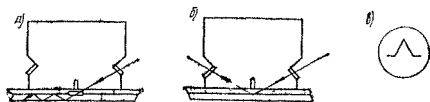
Схемы проверки качества сварного шва ультразвуком
